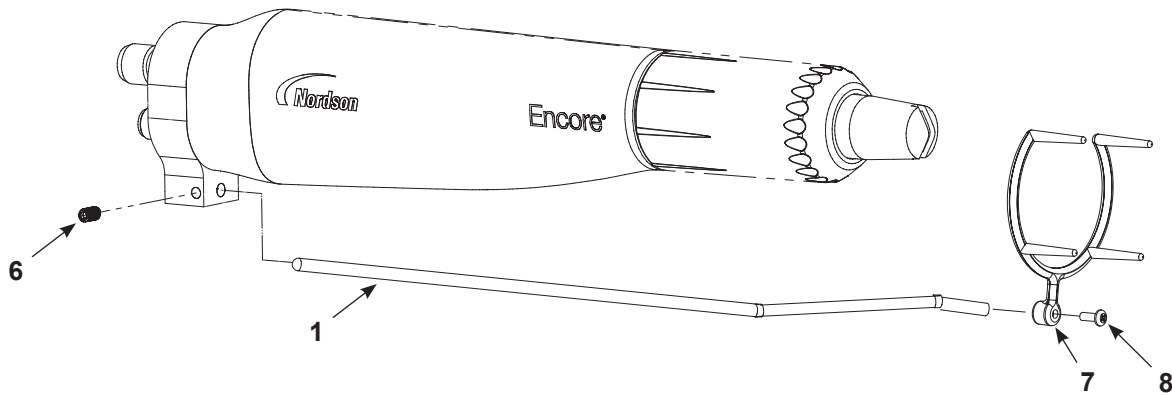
Installation du collecteur d'ions – Pistolet à fixation sur barre
